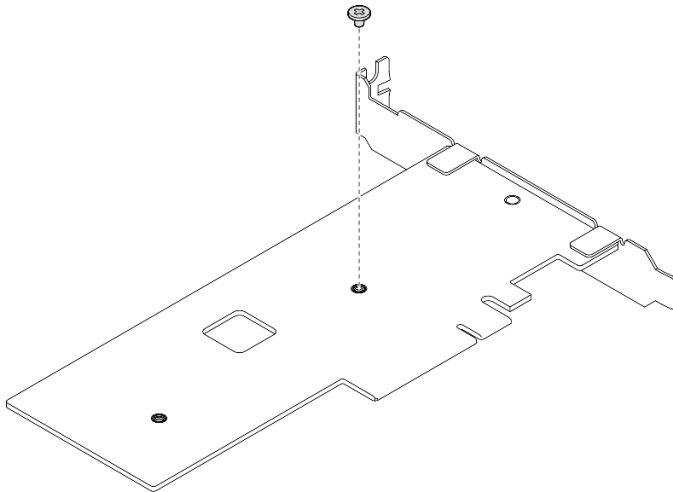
Entfernen der Schraube an der Rückseite des PCIe-Adapters
